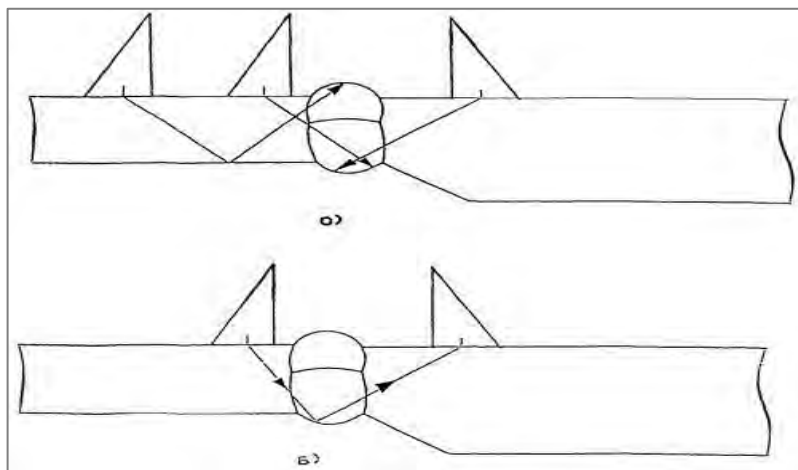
Принцип проведения ультразвукового контроля сварных соединений.
